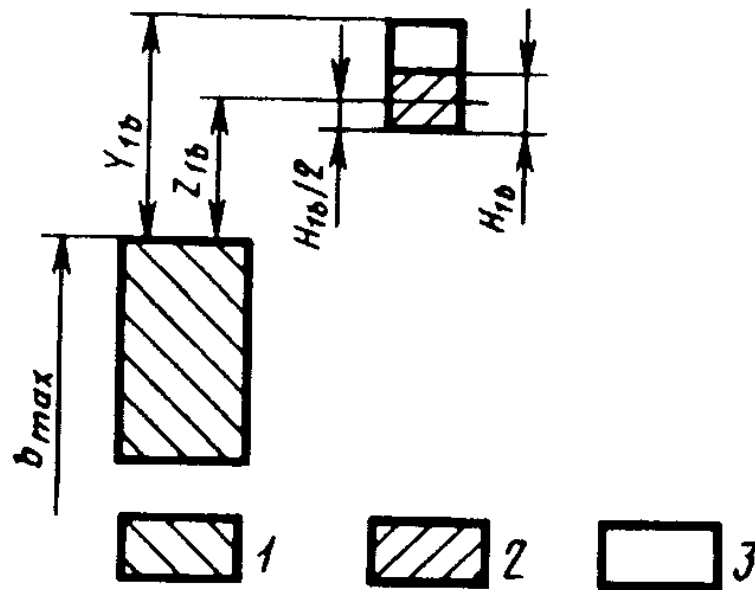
Расположение поля допуска размера b_k калибр-колец:
